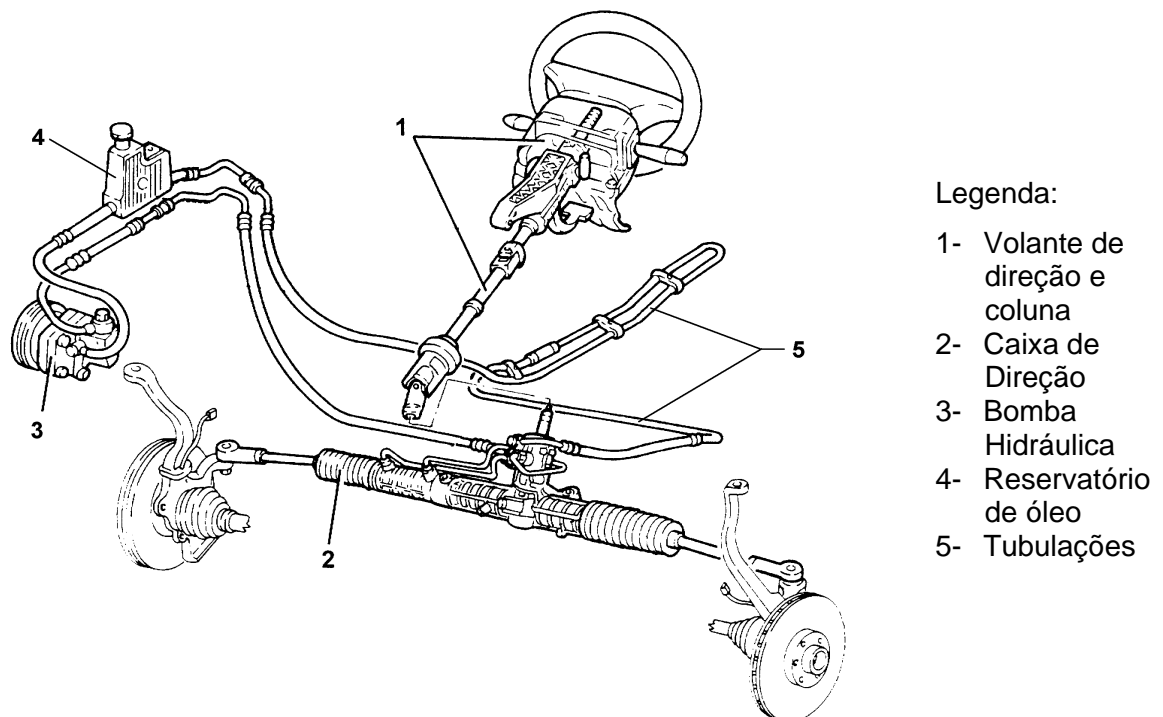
Esquema dos componentes do sistema de direção hidráulica.
